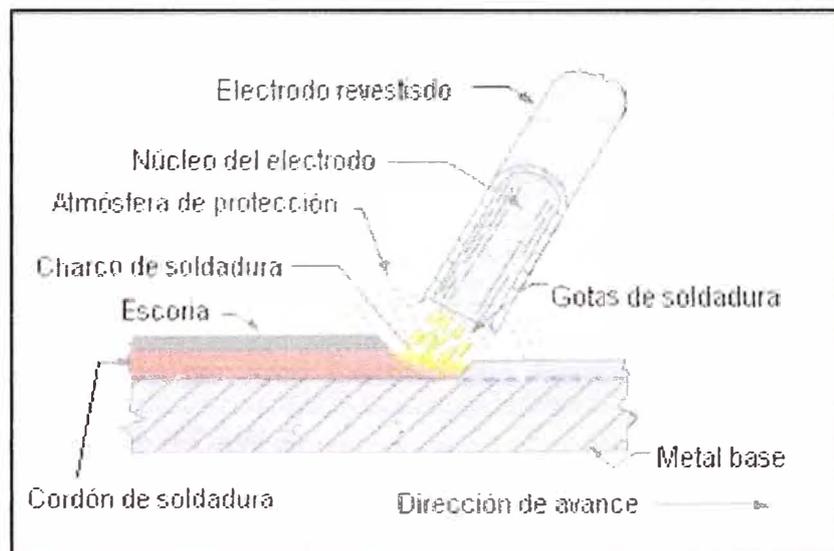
Proceso de Soldadura SMAW
